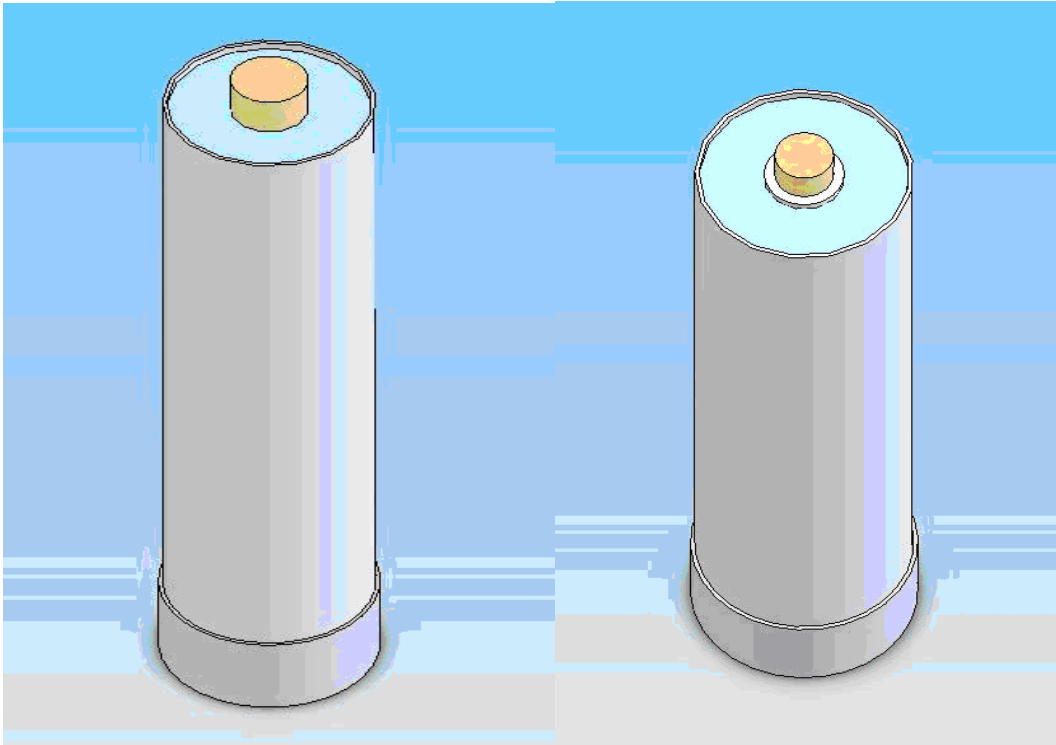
molde gesso, à esq. com o toro de 38 mm e à dir. com toro de 28 mm.
